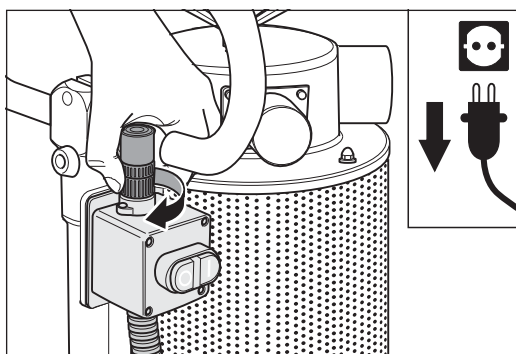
Den Gewinding des Kabelsteckers im Uhrzeigersinn am Ein-/Aus-Schalter festschrauben.
